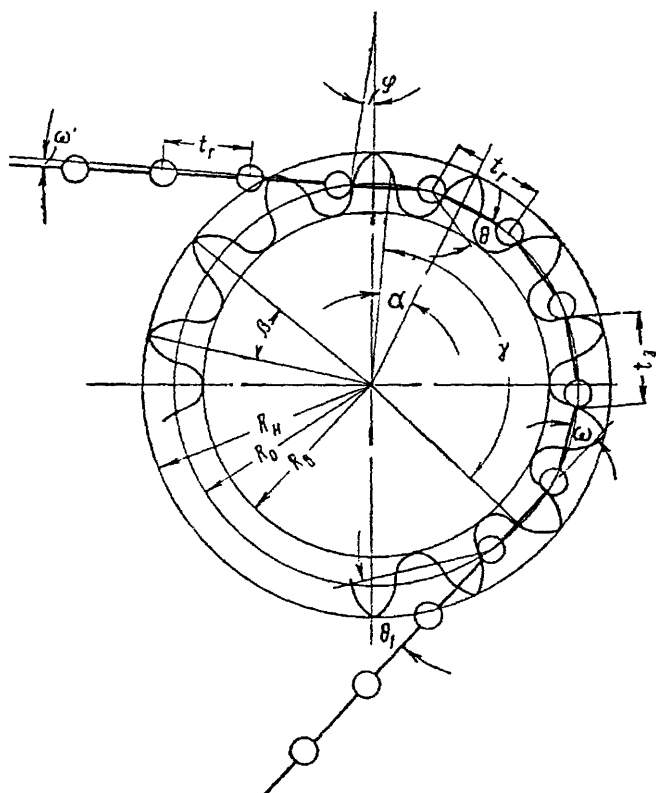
Типы зацепления ведущих колес с гусеничными цепями
